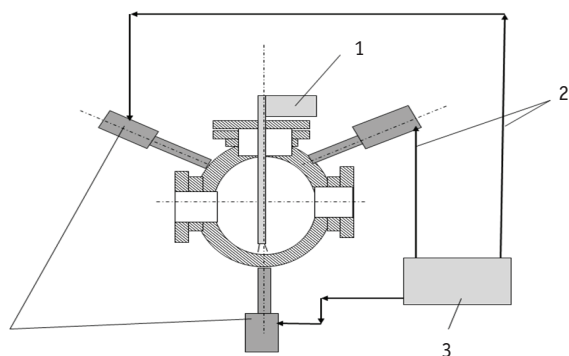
Схема устройства ультразвуковой обработки наплавки трубопроводной арматуры: 1 – сварочный автомат; 2 – линии связи; 3 – блок ультразвуковых генераторов
